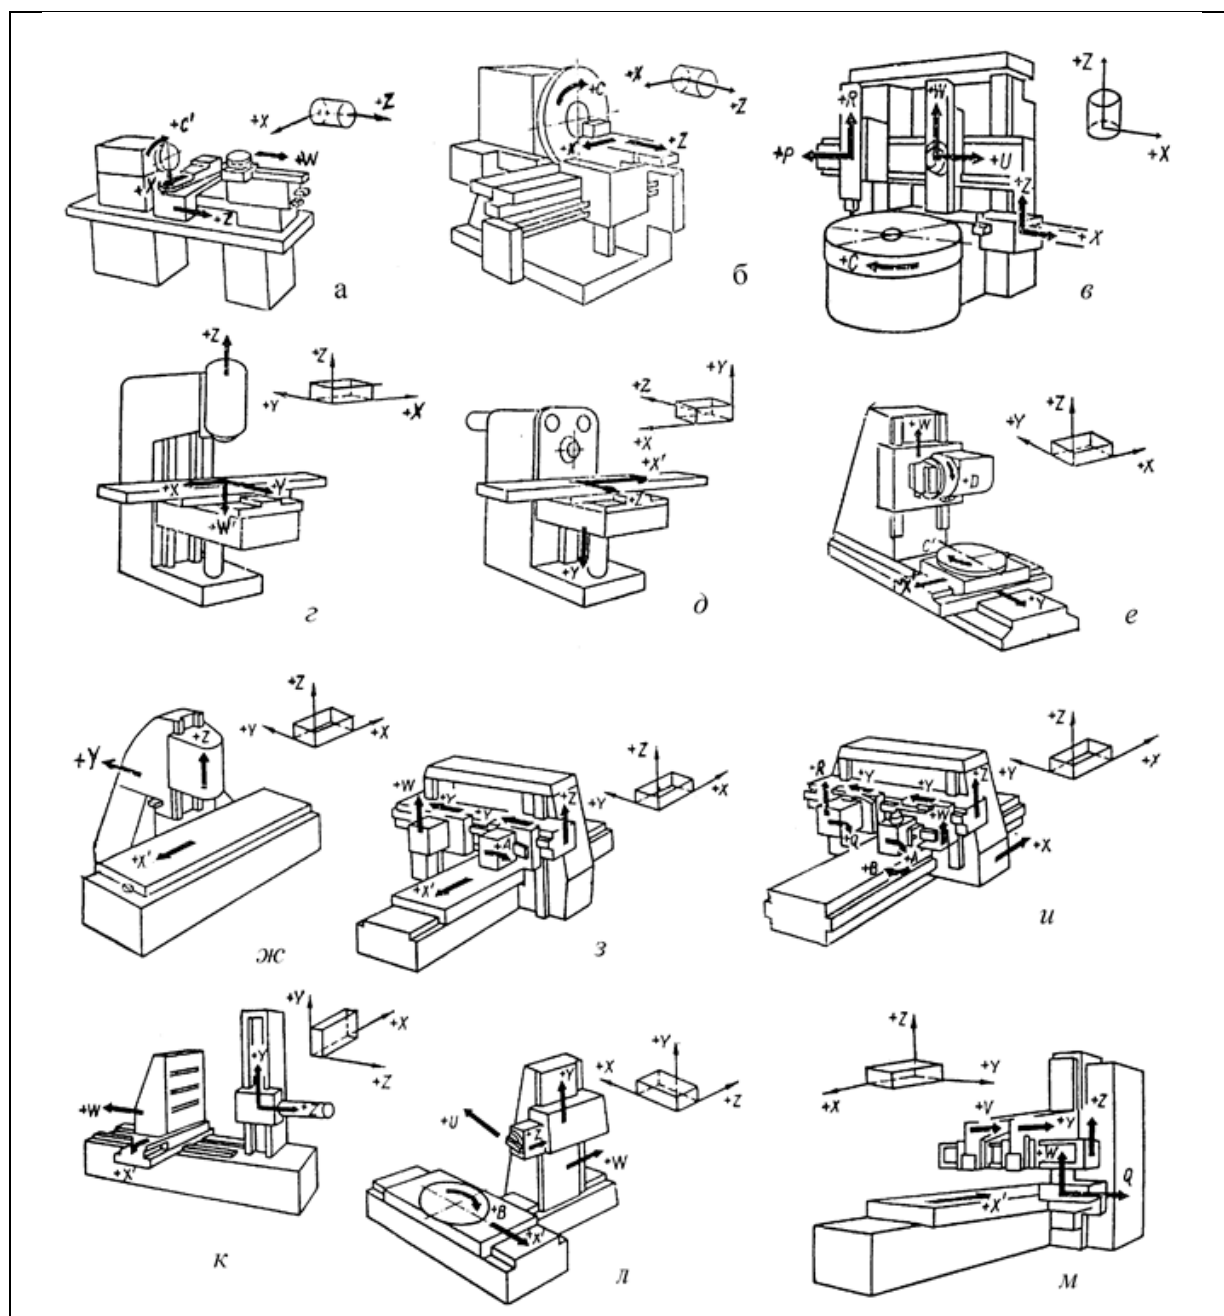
Обозначение осей координат и направлений перемещений на схемах станков с ЧПУ: *а* – токарно-револьверного; *б* – лоботокарного; *в* – токарно-карусельного; *г* – вертикально-фрезерного; *д* – горизонтального консольно-фрезерного; *е* – фрезерного с поворотным столом и поворотной бабкой; *ж* – вертикального портально-фрезерного; *з* – двухстоечного портально-фрезерного; *и* – двухстоечного с подвижным порталом; *к* – горизонтально-расточного с неподвижной передней бабкой; *л* – с продольно-подвижной передней бабкой; *м* – продольно-строгального
